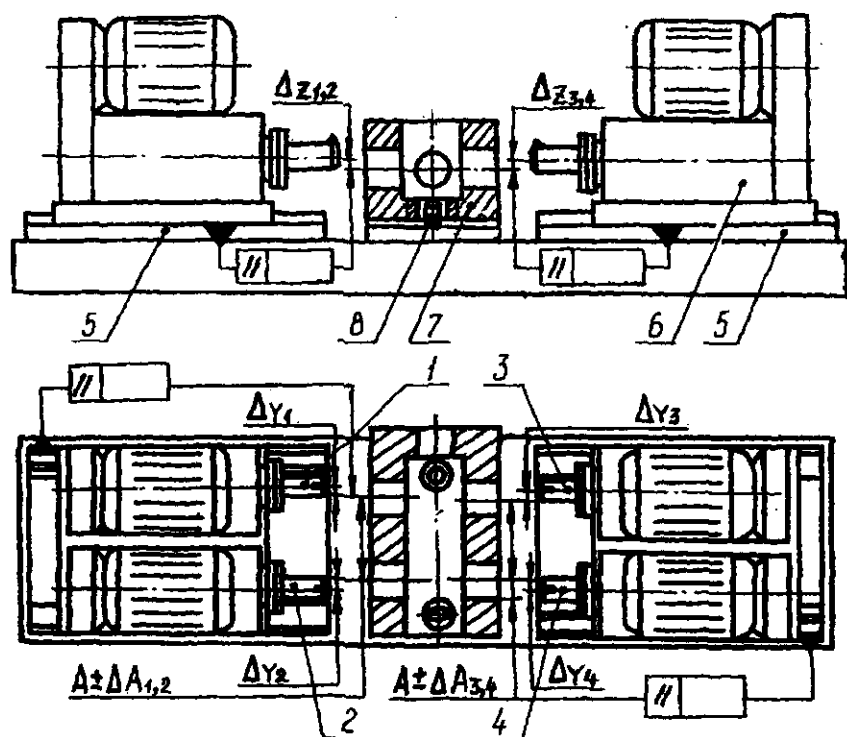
Компоновка двухстороннего четырехшпиндельного агрегатного станка: 1 – 4 номера шпинделей; 5 – силовые столы; 6 – унифицированная расточная бабка (6 шт.); 7 – эталонная деталь; 8 – приспособление; $\Delta y_1, \Delta y_2$ – отклонения осей шпинделей по соответствующим координатам; ΔA – отклонения межосевых расстояний
